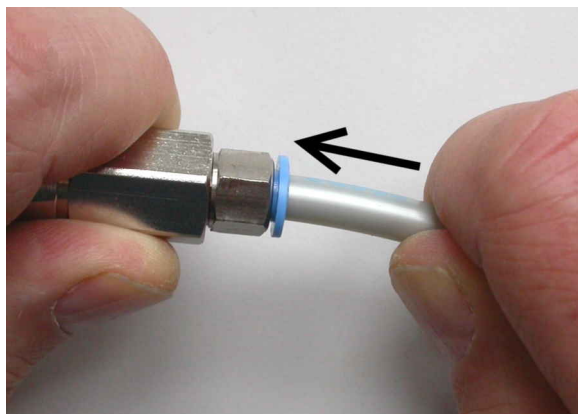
Montaje del adaptador push-pull (izquierda) y el tubo de 6 mm (derecha)
